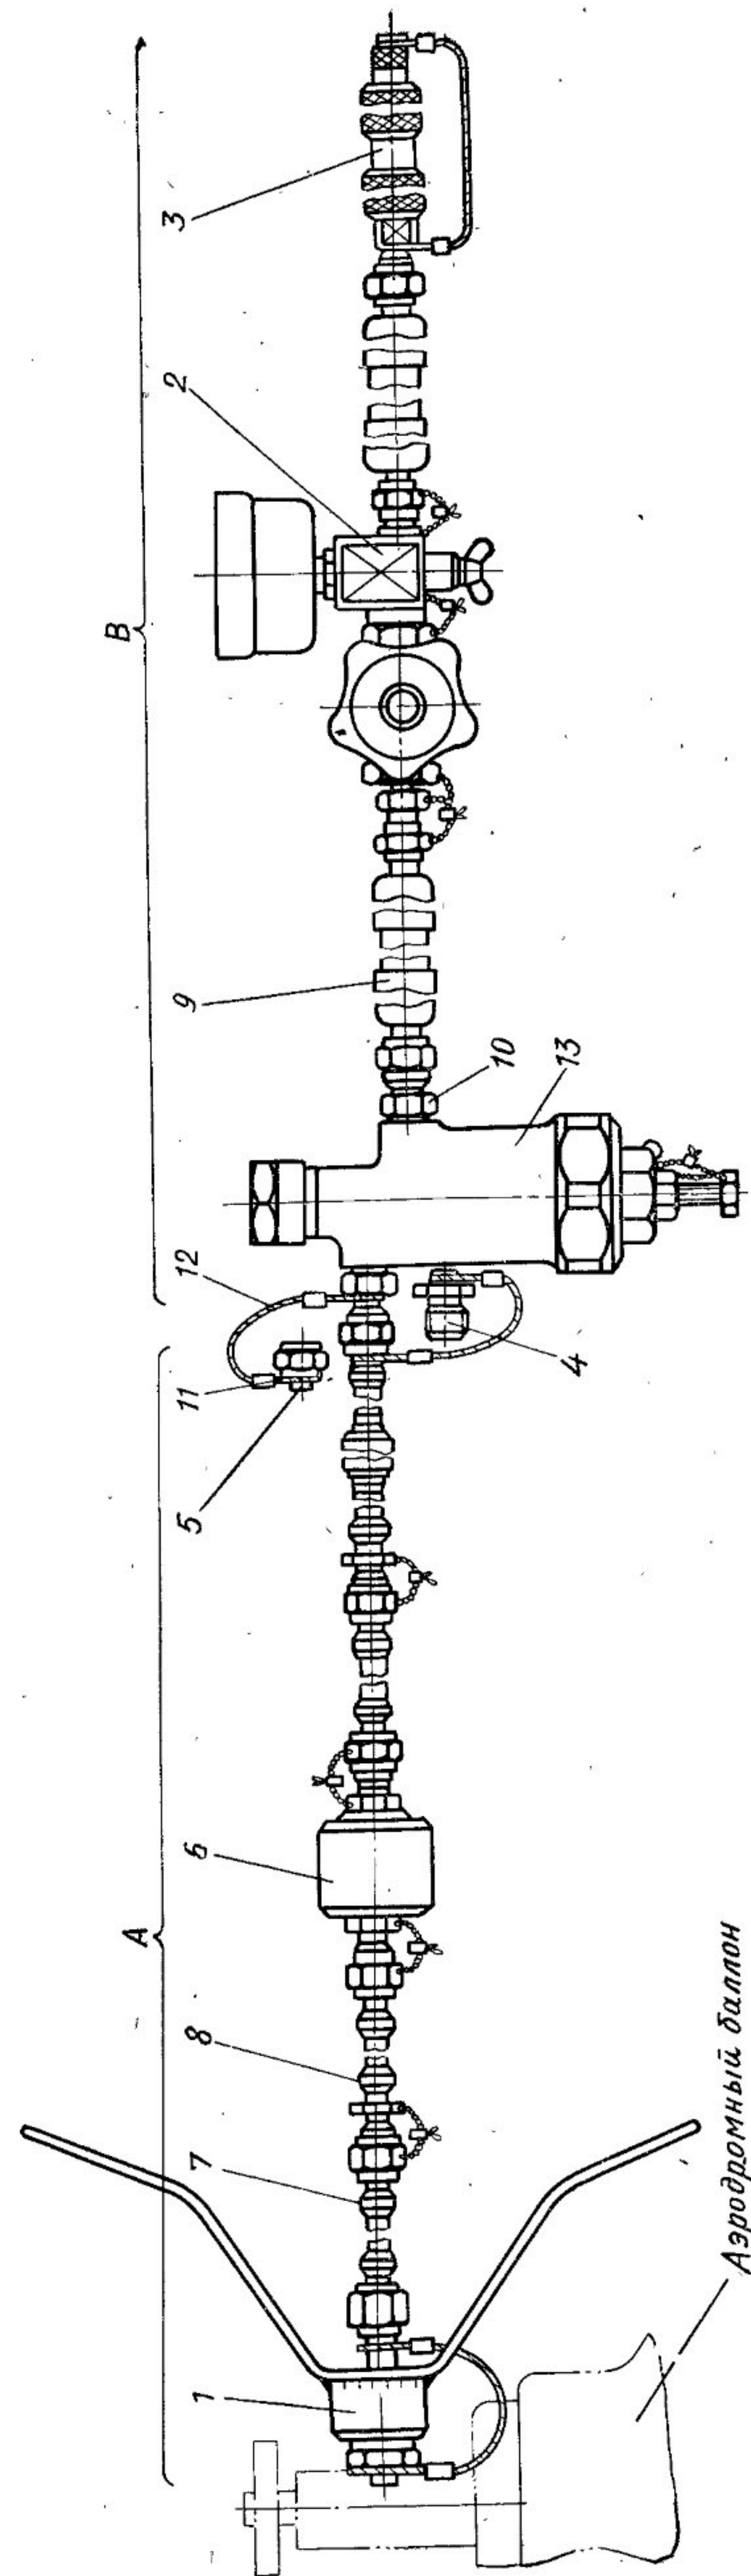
Приспособление для зарядки бортсети, гидроаккумуляторов, амортизационных стоек шасси и камер колес (вариант III сборки приспособления для зарядки бортсети):
